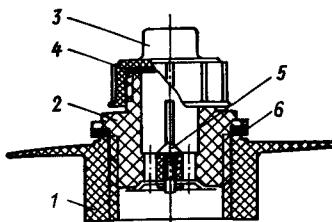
Корпус вентиля с эластичным лепестковым клапаном
